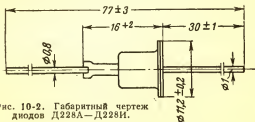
Габаритный чертеж диодов Д228А—Д228И.
